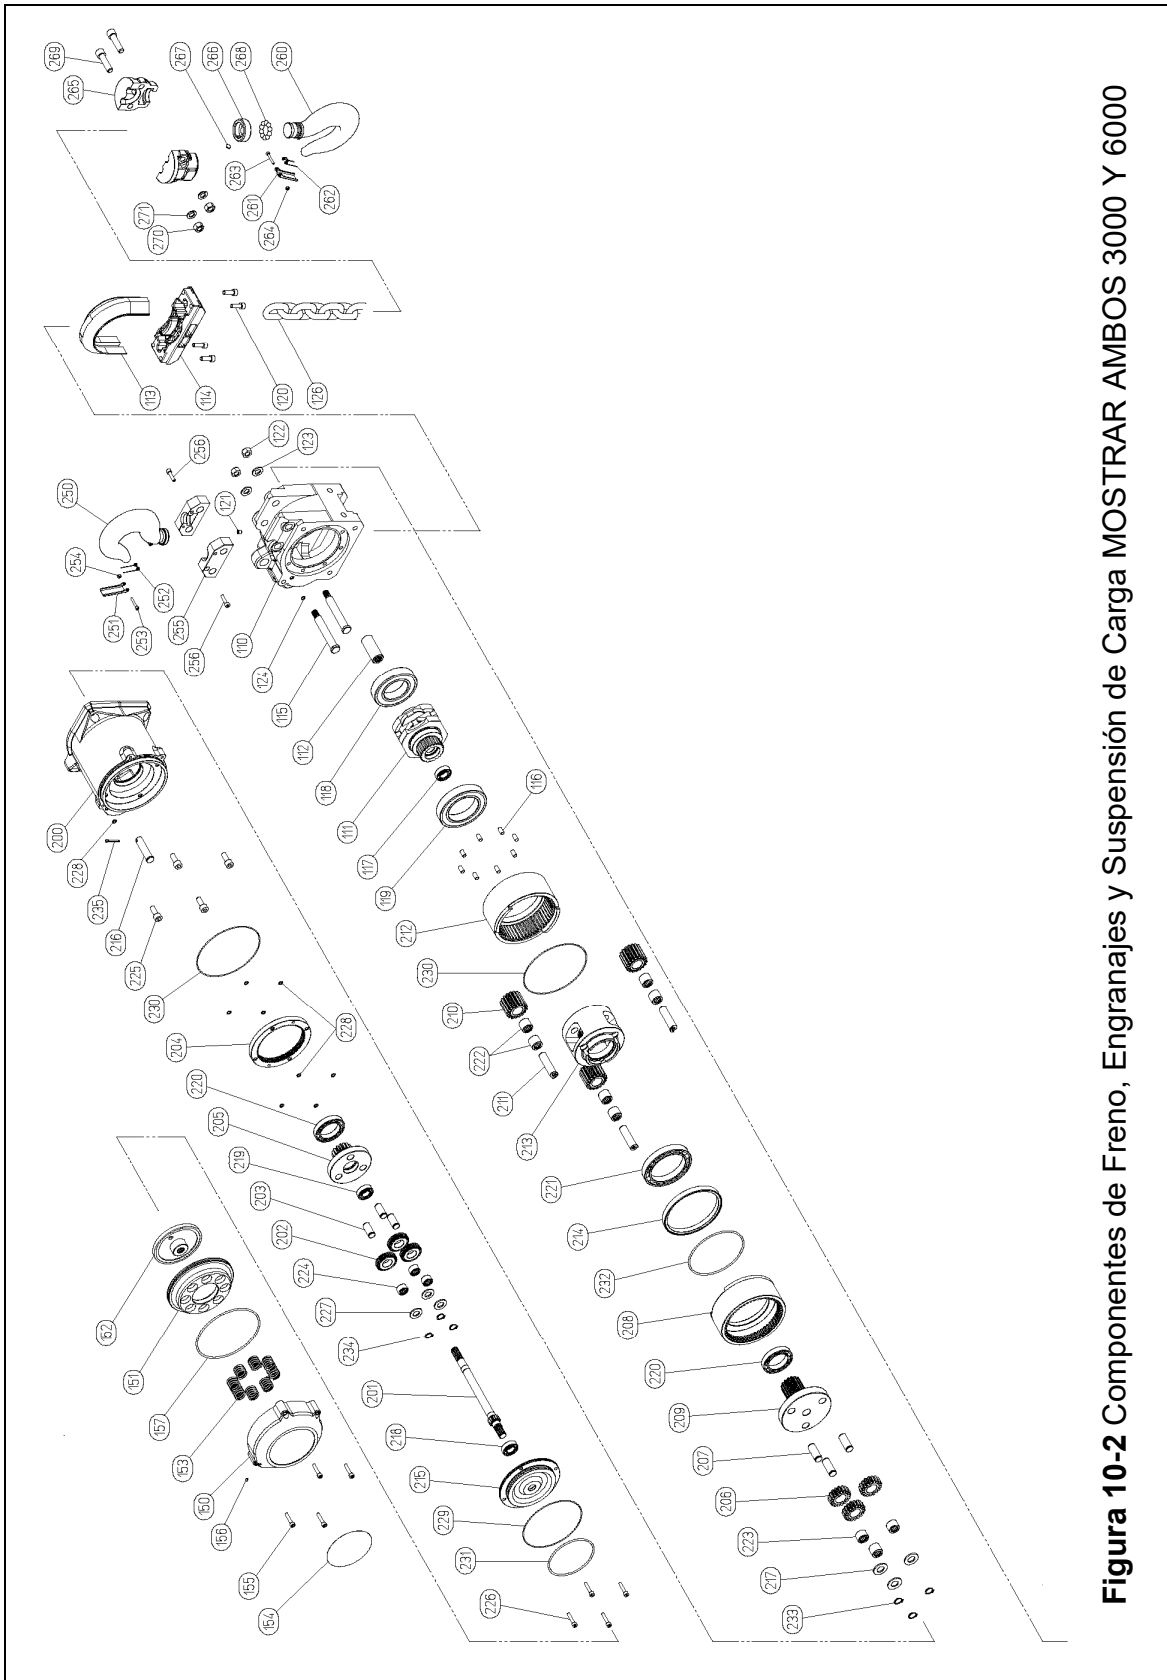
Componentes de Freno, Engranajes y Suspensión de Carga MOSTRAR AMBOS 3000 Y 6000
